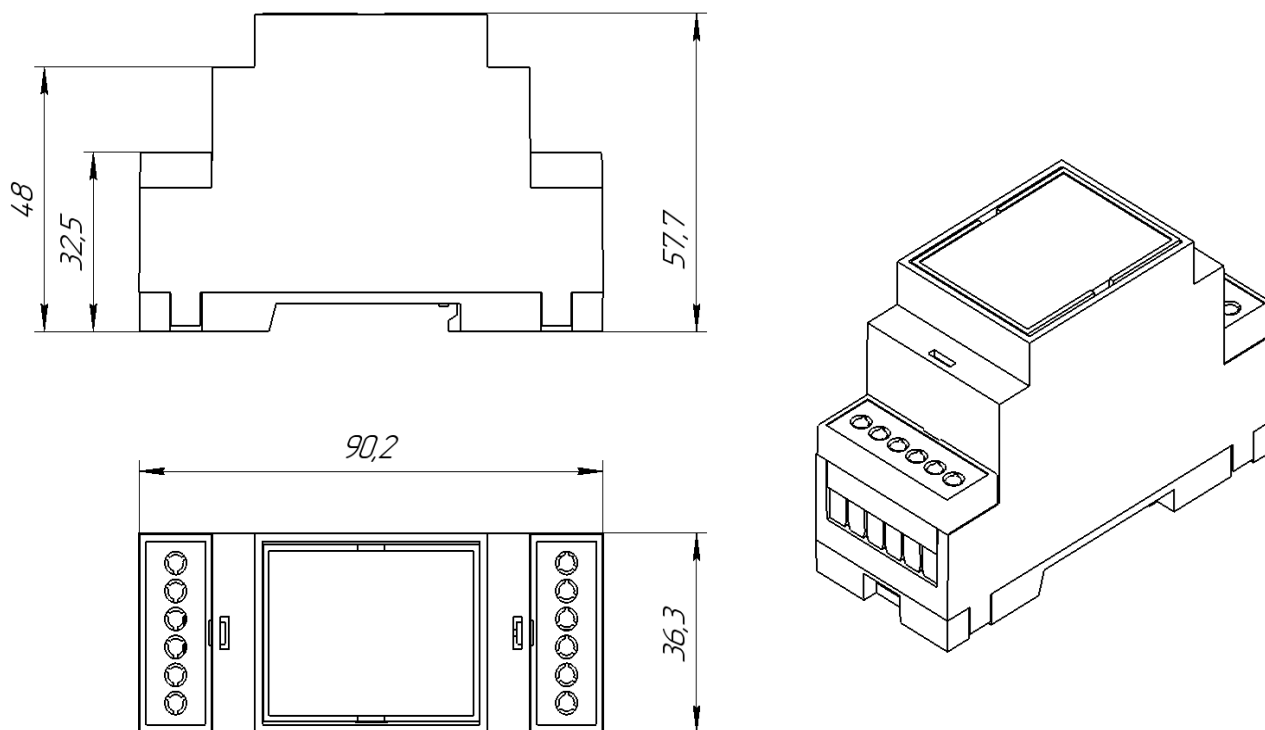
Габаритные размеры корпуса преобразователя интерфейсов
